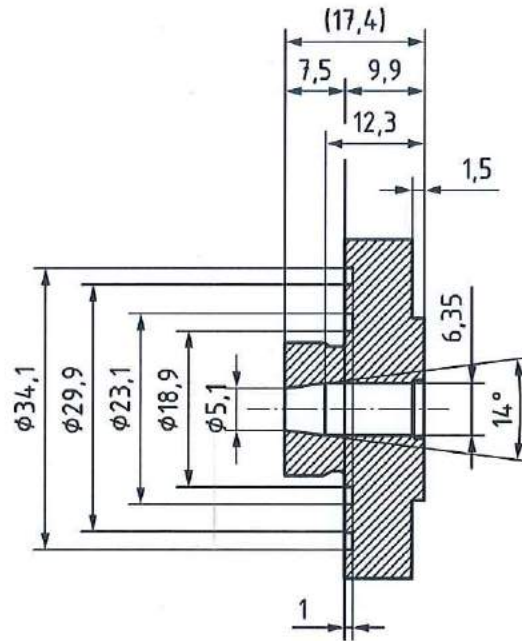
Insert de la chambre à cartouche pour Type 6,3/16
